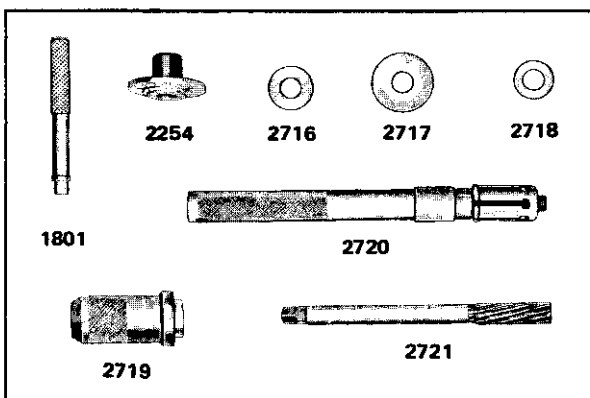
Spezialwerkzeuge für Arbeiten am ausgebauten, mech. Lenkgetriebe
